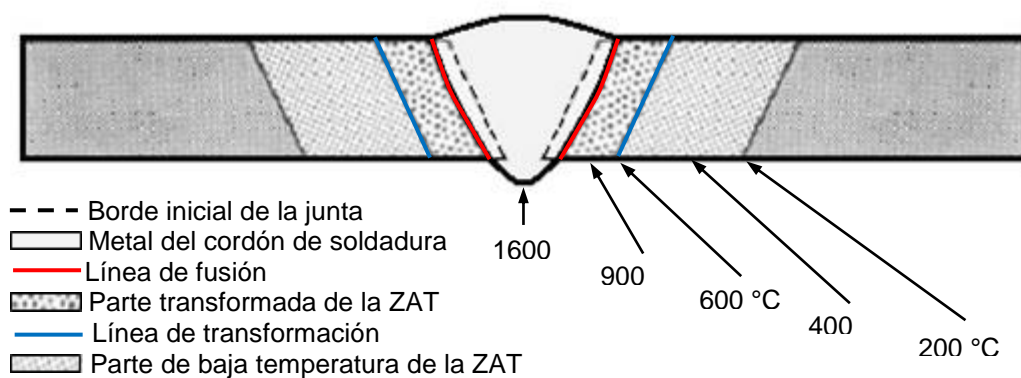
Esquema de las zonas y líneas características de una junta soldada [4].
